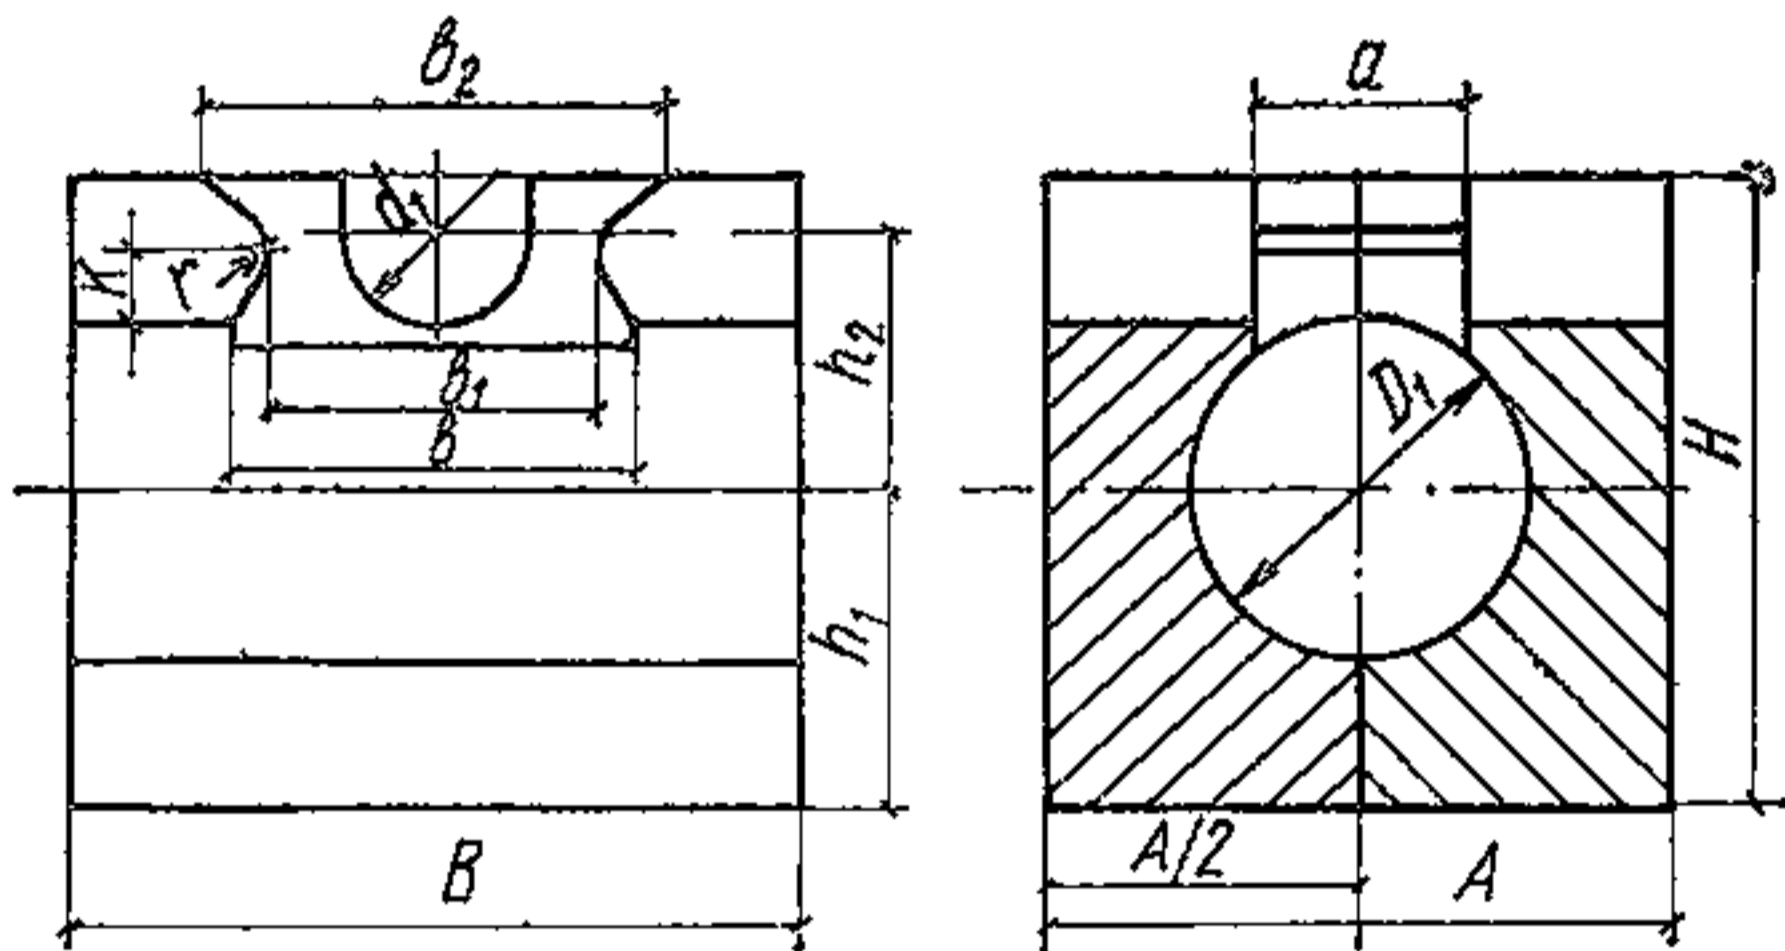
Конструкция медных форм для сварки крестовых соединений стержней с горизонтальным положением швов
